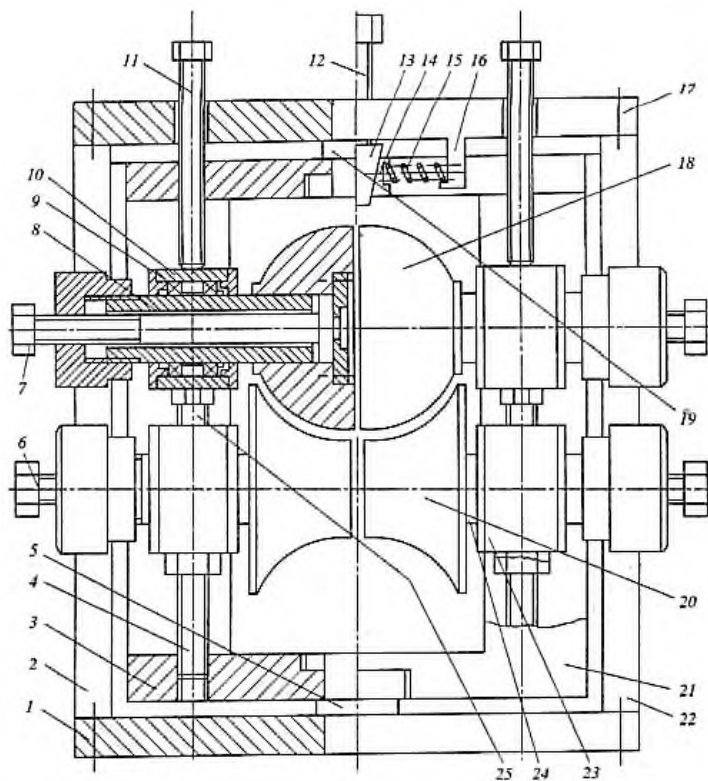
Горизонтальная клеть трубоформовочного стана [9]
